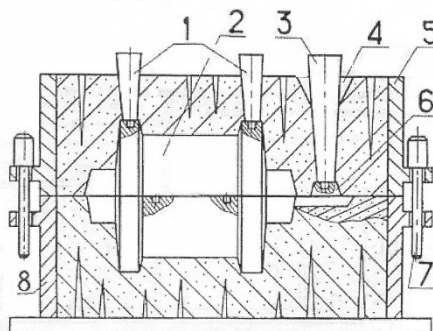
Набитые верхняя и нижняя опоки – полуформы: 1 – модели выпоров; 2 – модель отливки; 3 – модель стояка; 4 – литниковая чаша; 5 – верхняя опока; 6 – модель шлакоуловителя; 7 – центрирующий штырь; 8 – нижняя опока
